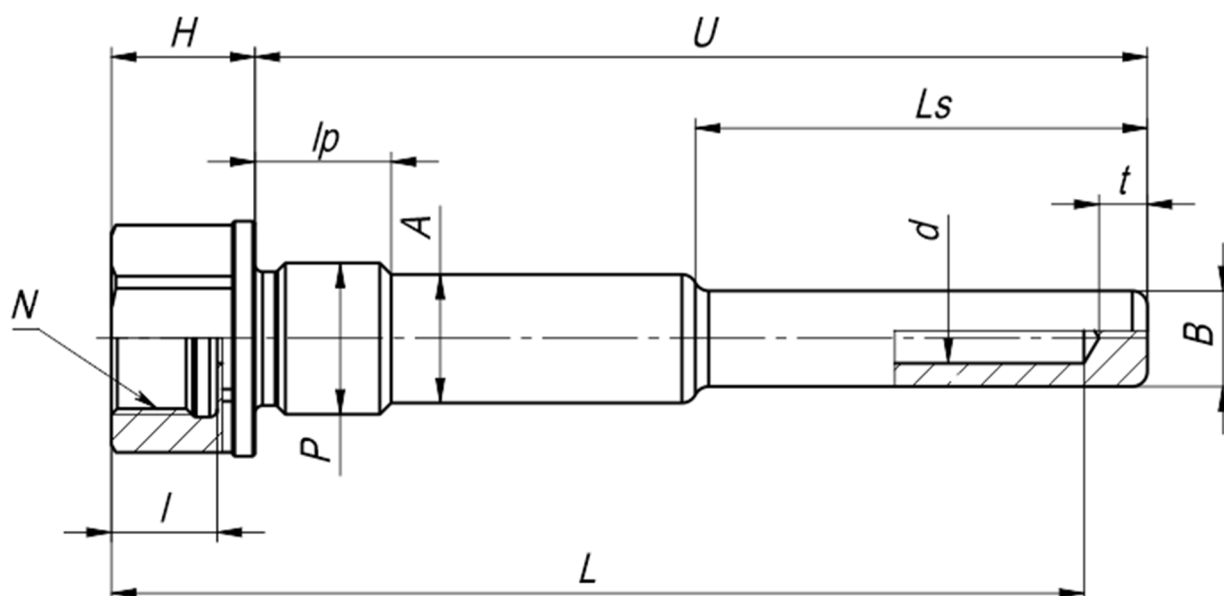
Гильза резьбовая, цельноточёная, ступенчатая под неподвижный шуцер.
